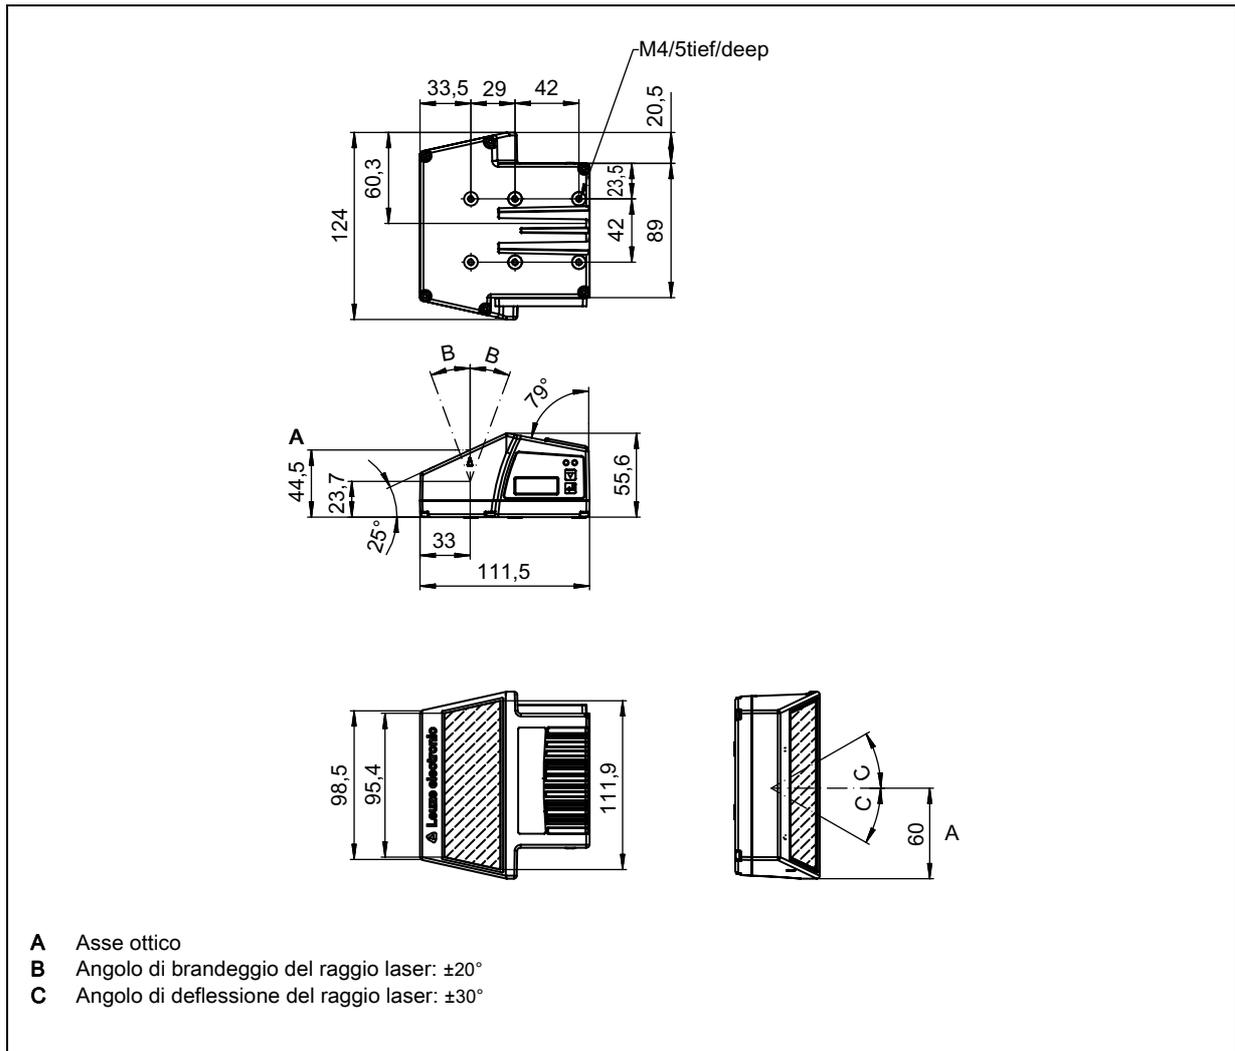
Disegno quotato scanner a specchio oscillante BCL 338/O...100
